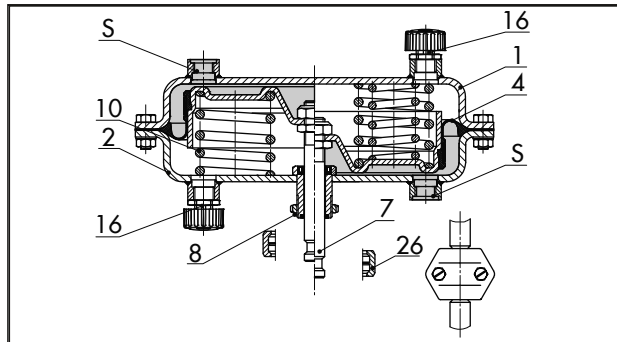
Tipo 3271 · Lado derecho con resortes adicionales
